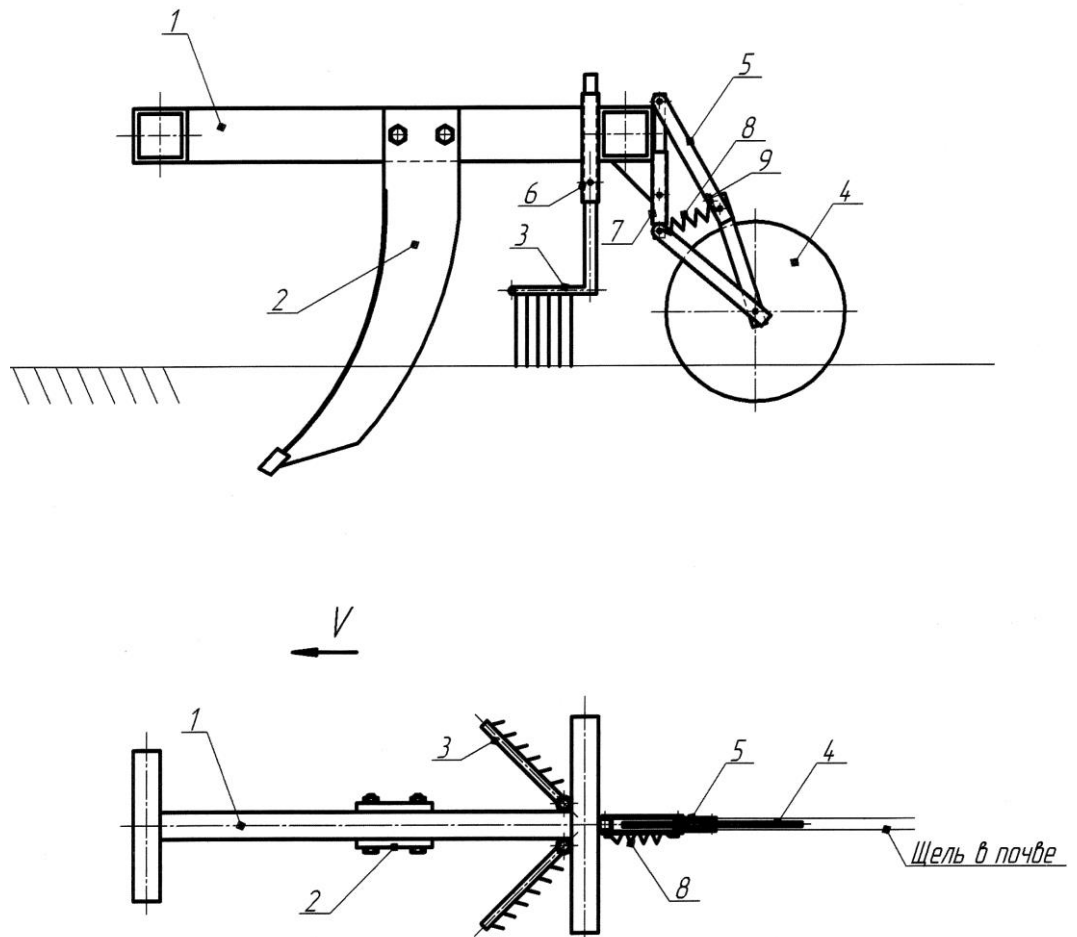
Схема экспериментального сельскохозяйственного агрегата: 1 – сварная рама; 2 – рабочий орган (щелерез); 3 – граблины соломонаправителя; 4 – соломозаделывающий диск; 5 – параллелограммный механизм; 6, 7 – устройства для регулировки; 8 – пружина; 9 – ограничитель
